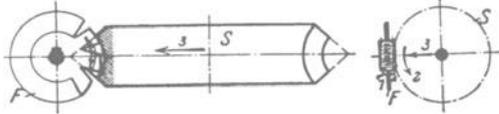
u. 306. Fräsen von Schneckenrädern.
